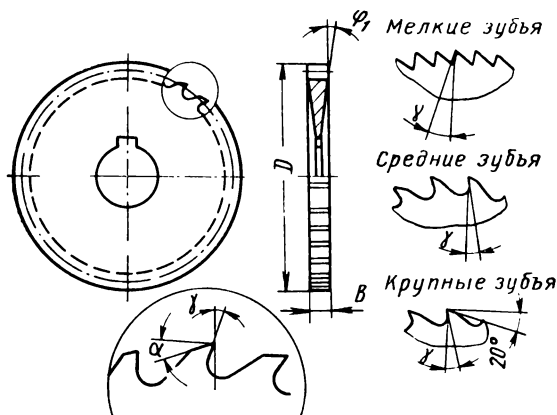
Фреза прорезная (шлицевая) и отрезная
